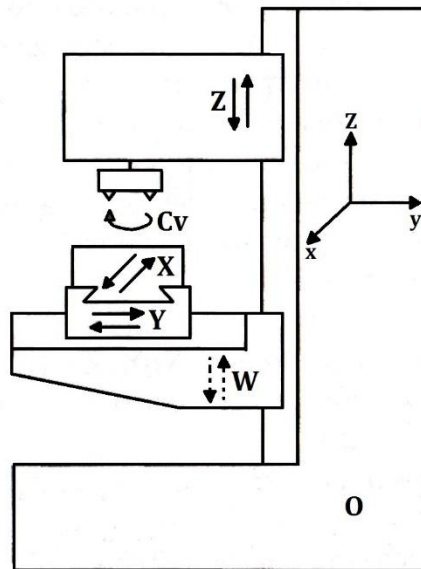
Компоновочная схема вертикально-фрезерный станка
